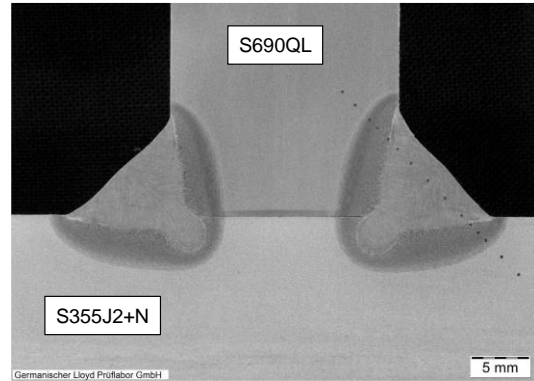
Makroschliff einer Stirnkehlnaht
